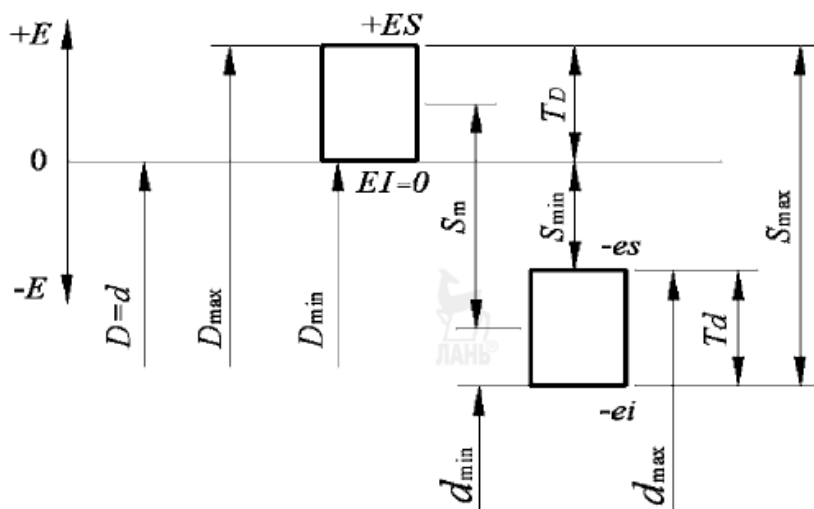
Схема расположения полей допусков посадок с зазором
